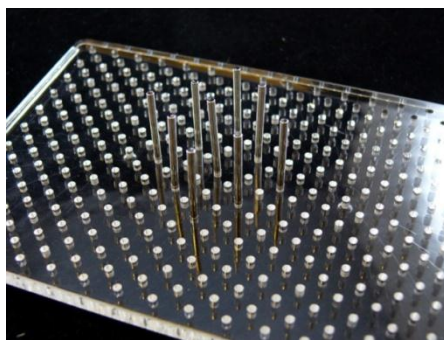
Приспособление для гибки проволоки *Wig Jig
